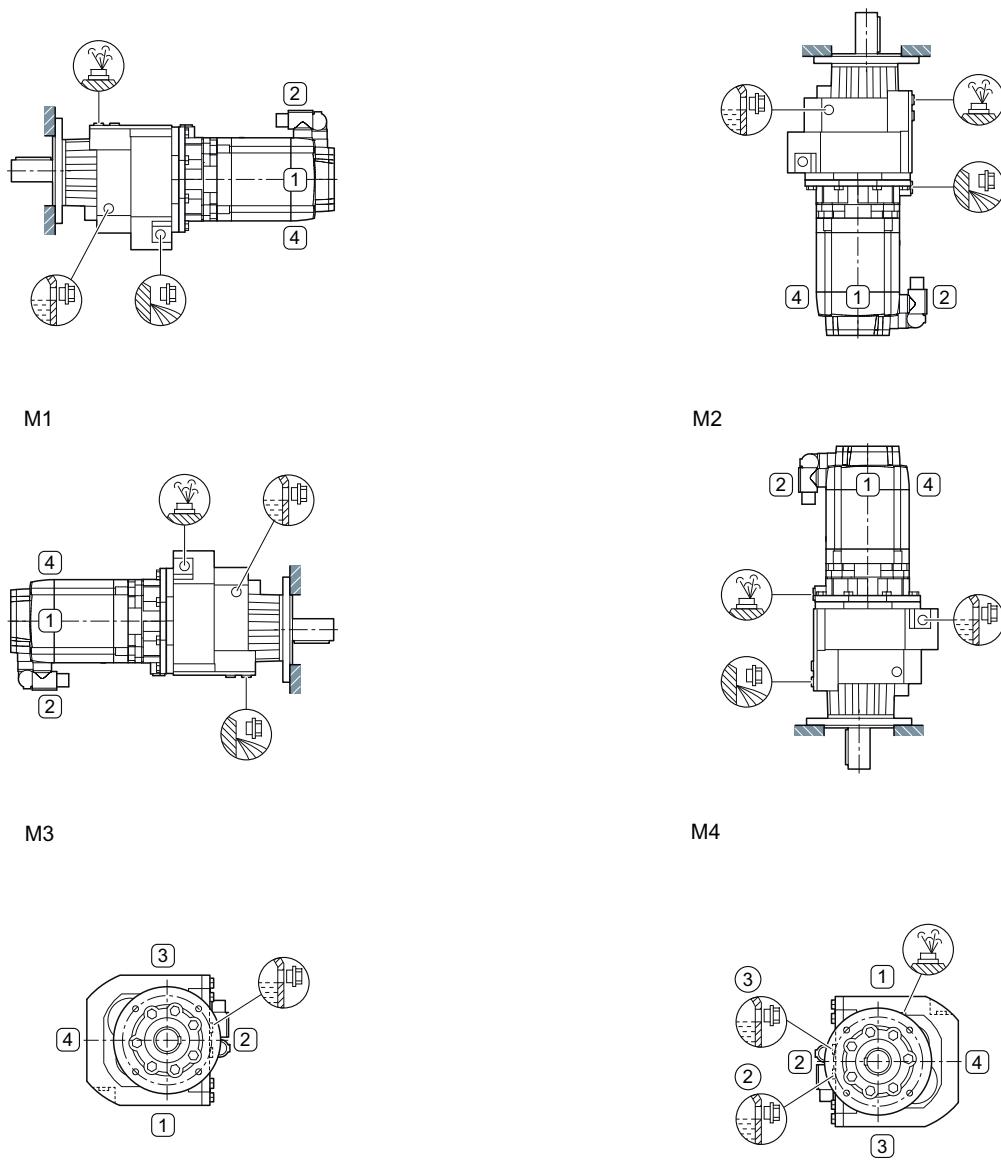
Einbaulagen für Servo-Stirnradriebemotoren DF und ZF (Flanschausführung) oder DZ und ZZ (Gehäuseflanschausführung), Baugrößen 19 - 29, 2-stufig und 3-stufig
